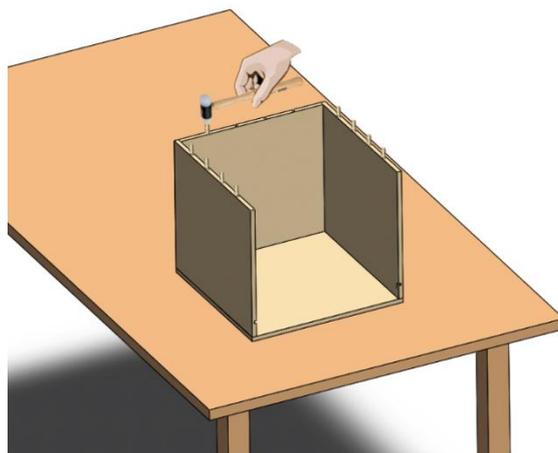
Paso 9 del ensamblaje del cajón (conjunto 2)
